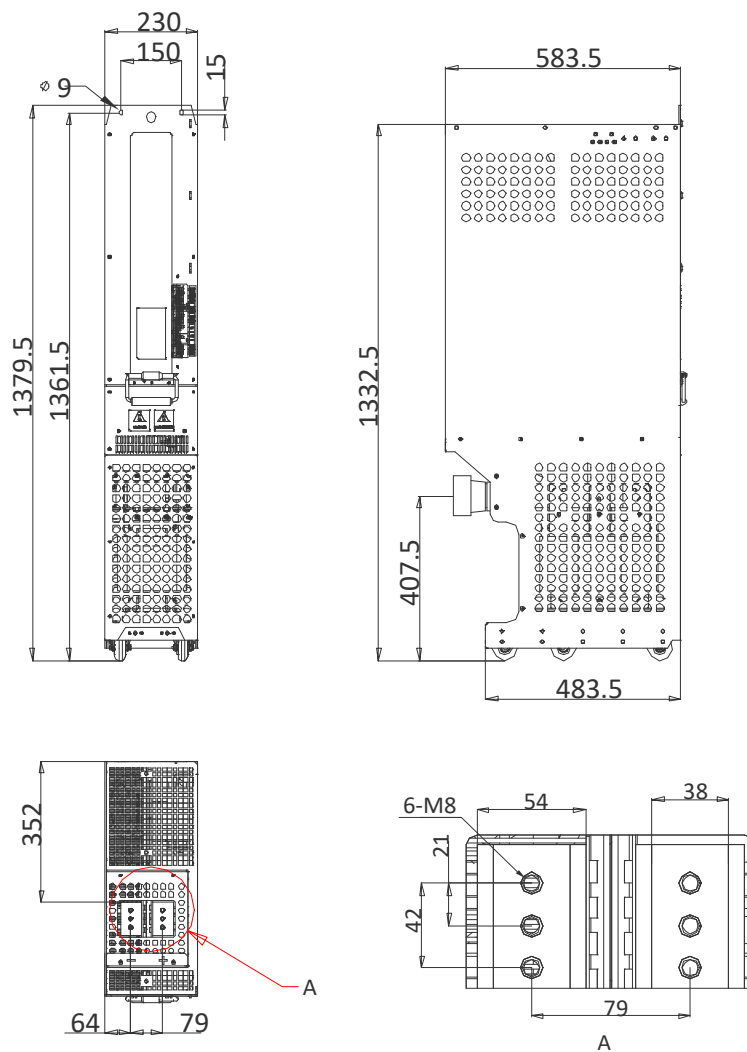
Габаритные размеры инвертора корпуса FR8 (мм)
